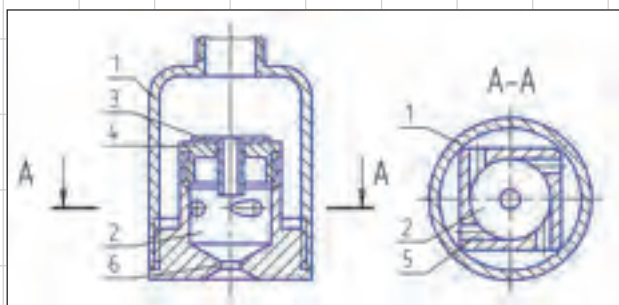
Эскиз центробежно-струйной форсунки: 1 — корпус форсунки; 2 — камера смешения; 3 — втулка осевого канала, 4 — крышка камеры смешения; 5 — тангенциальный канал, 6 — сопловое отверстие
